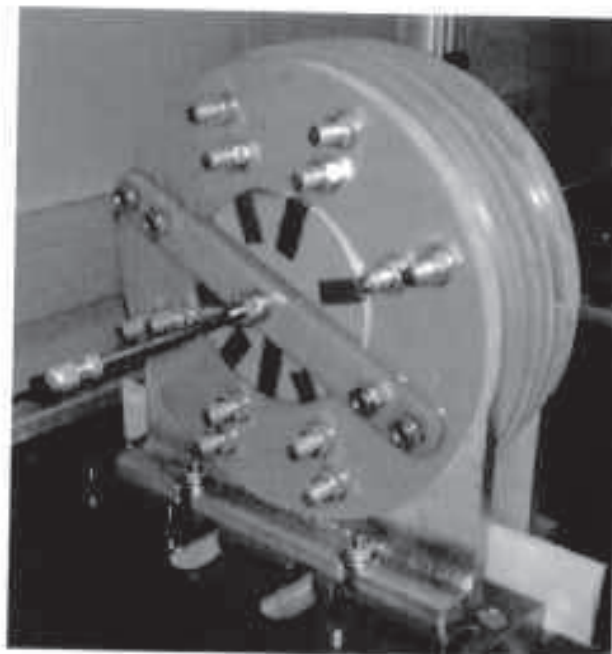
Ensamblaje de concentrador de campo y dispositivo eyector de pieza de trabajo
